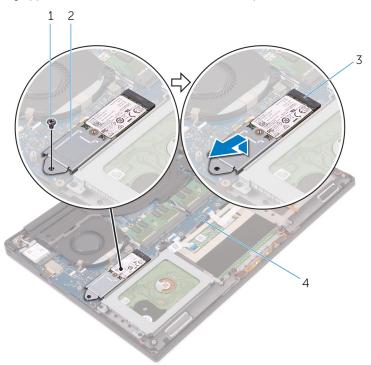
Entfernen der SSD-Laufwerk-Baugruppe
